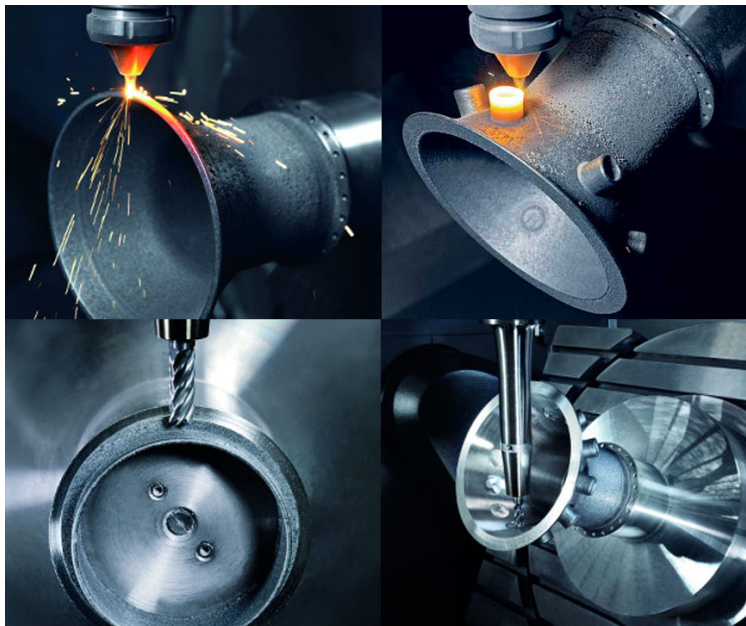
Fabricación de carcasa de turbina por Laser Cladding y mecanizado CNC en una máquina híbrida. Recuperado a partir de <http://es.dmgmori.com/productos/lasertec/manufacturing/mar14/pics/DMG-MORI-LASERTEC-65-AdditiveManufacturing-5.jpg>
